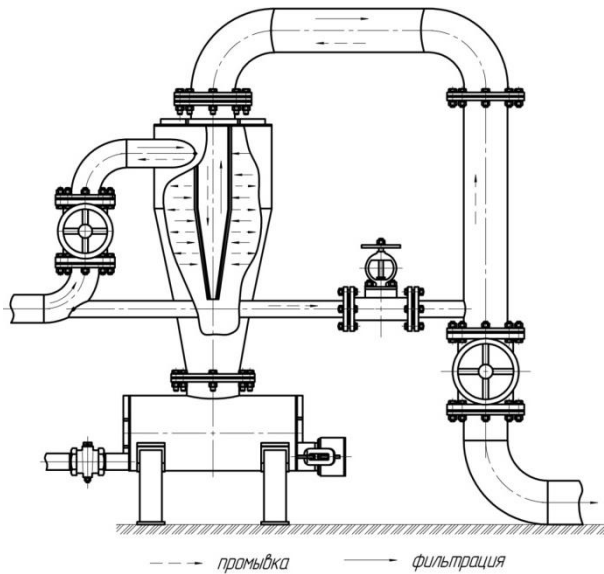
Установка для грубой и тонкой очистки поливной воды
